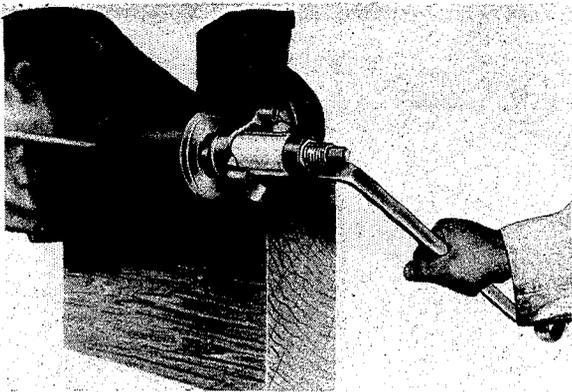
Einbauwerkzeug für Kreuzgelenkflansch
